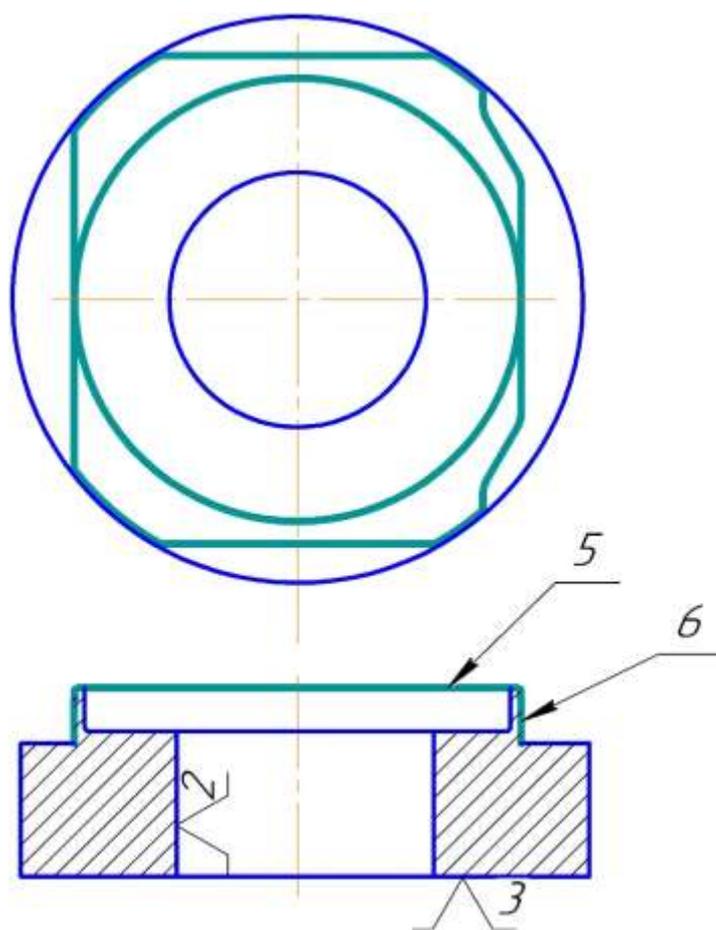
эскиз для фрезерной операции с ЧПУ 015.
